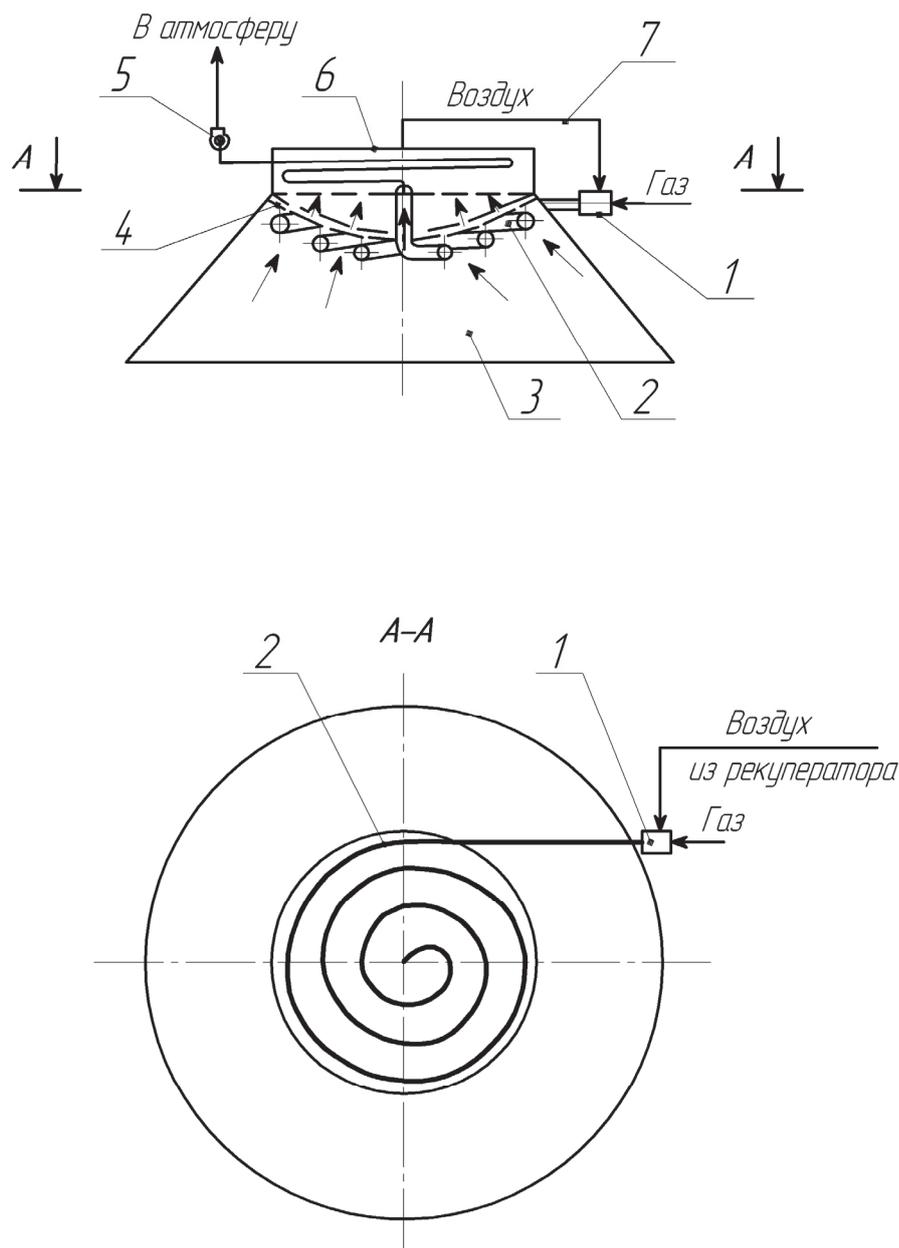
Схема нового энергоэффективного инфракрасного газового трубчатого нагревателя закрытой конструкции: 1 – газовая горелка; 2 – трубчатый излучатель; 3 – боковая часть отражателя тепловых потоков; 4 – двухслойная перфорированная часть отражателя тепловых потоков; 5 – вентилятор; 6 – газоздушный рекуператор; 7 – воздухопровод
